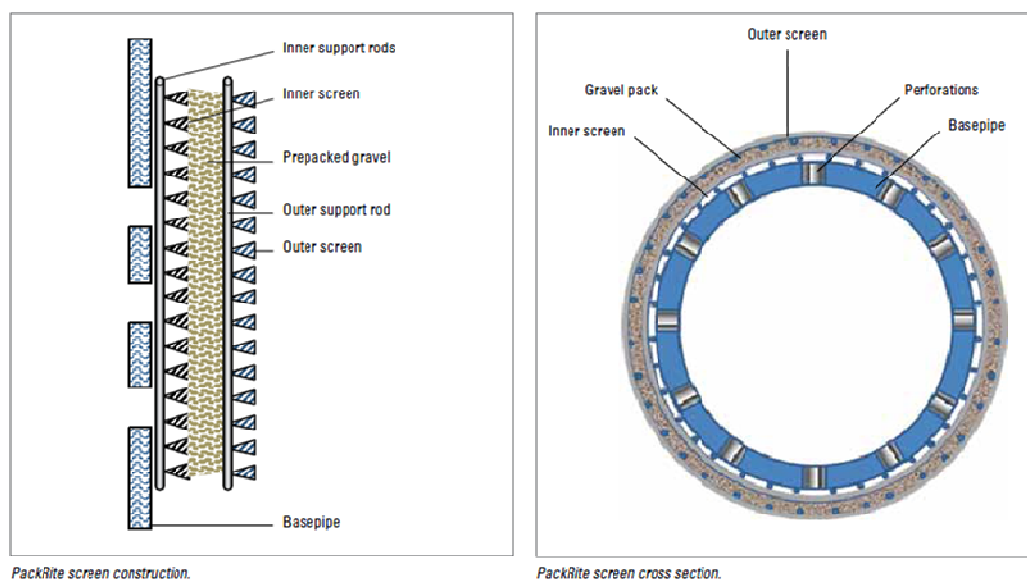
Detalhes de seções do Tubo Telado Pré-empacotado.
